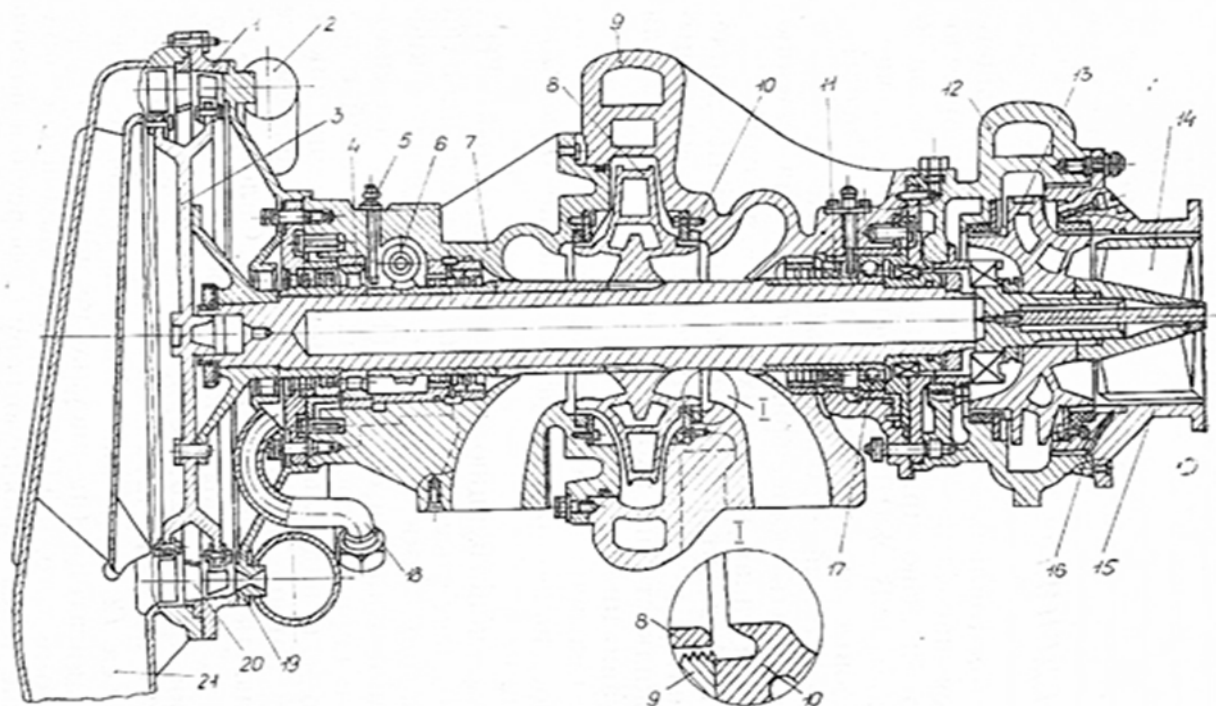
ТНА самолетного ЖРД : 1 - корпус турбины; 2 - коллектор подвода парогаса; 3 - диск турбины; 4 - радиальный подшипник; 5 - подвод масла для смазки подшипника; 6 - червячная пара привода маслонасоса; 7 - крышка насоса окислителя; 8 - колесо насоса окислителя; 9 - корпус насоса окислителя; 10 - уплотнение по борту крыльчатки; 11 -
